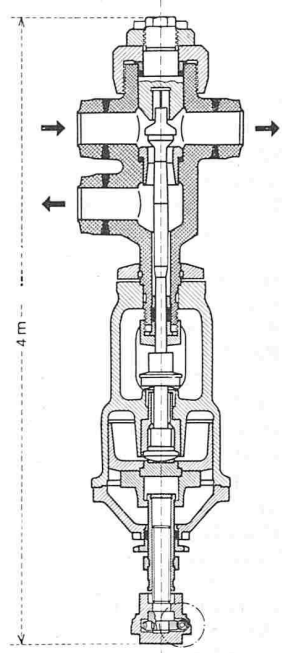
(rechts). Druckölgesteuertes Dampfabgabeventil
